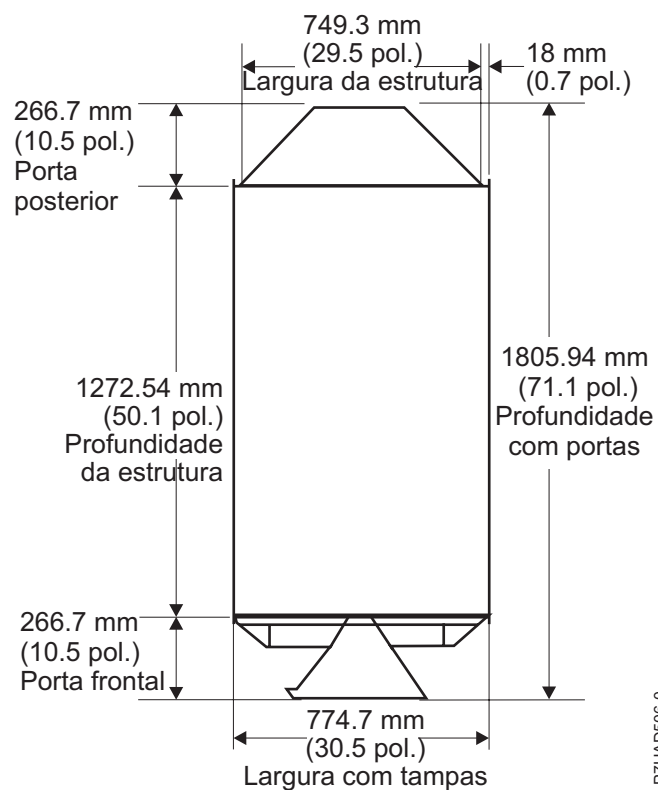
Vista de plano para sistema de estrutura única com portas acústicas
